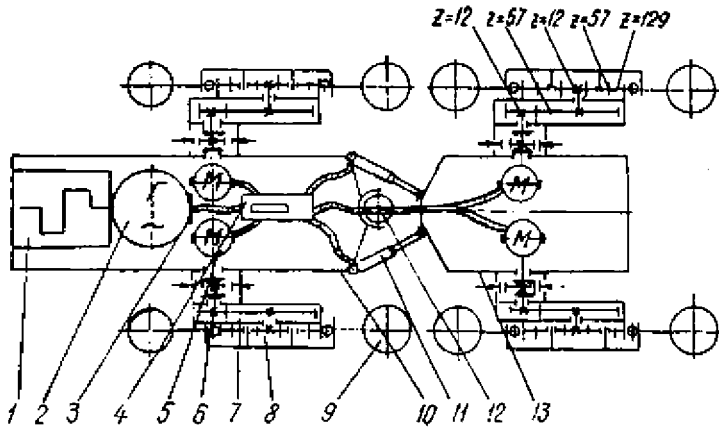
Принципиальная схема колесного трактора: 1 – двигатель; 2 – генератор; 3 – соединительные провода; 4 – блок управления; 5 – тяговый электродвигатель; 6 – тормоз свободного хода; 7 – промежуточный редуктор; 8 – колесный редуктор; 9 – колеса; 10 – полурама силового модуля; 11 – электромеханизмы; 12 – поворотное устройство; 13 – полурама технологического модуля
